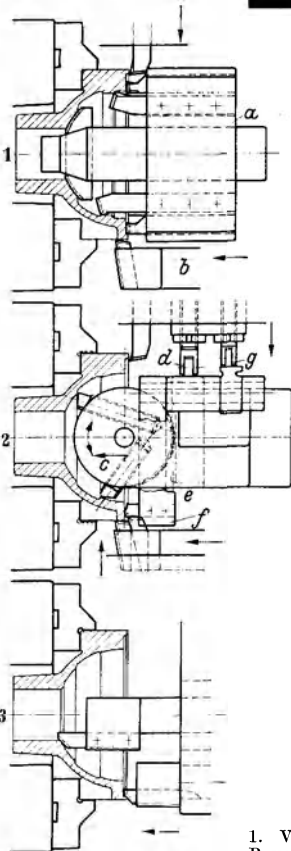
Ansicht der Werkzeugeinrichtung für das Arbeitsbeispiel nach Abb. 112.
